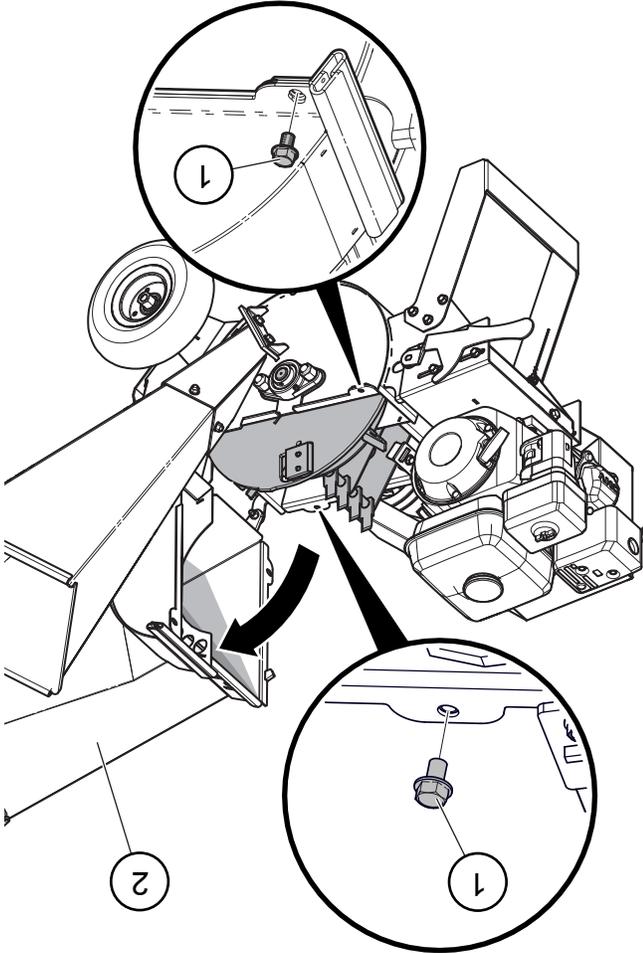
Ouvrir le compartiment supérieur du rotor
